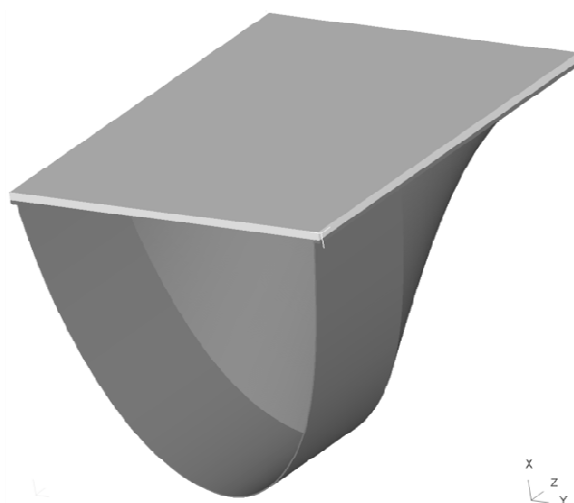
Сечение матрицы для формовки обтекателя корпуса авиадвигателя и исходной заготовки. МКЭ-модель.
